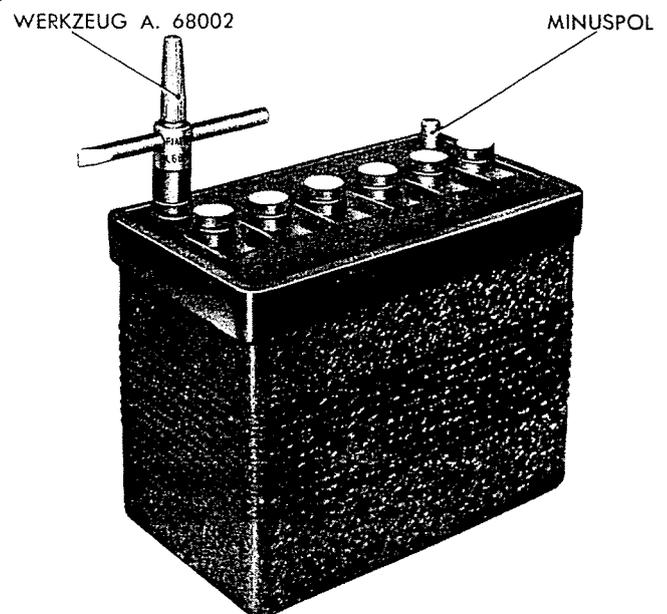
Reinigung der Polköpfe mit dem Werkzeug A. 68002.
